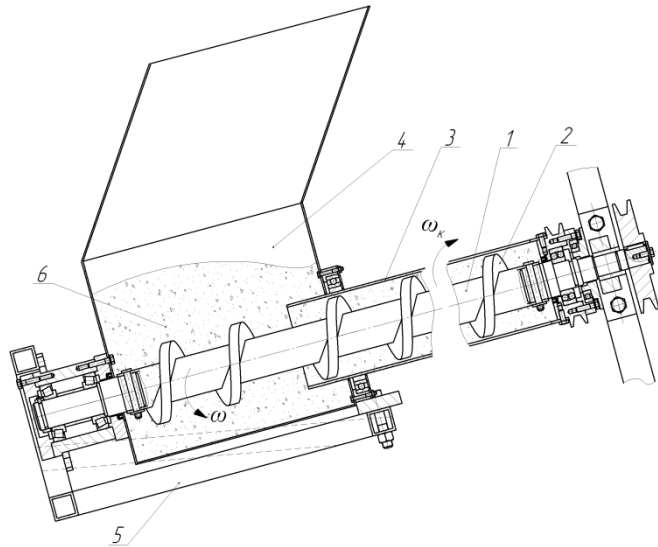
Конструкційна схема гвинтового конвеєра з обертовим кожухом: 1 – привідний вал; 2 – гвинтовий робочий орган; 3 – обертовий кожух; 4 – бункер; 5 – рама; 6 – матеріал, що переміщується
